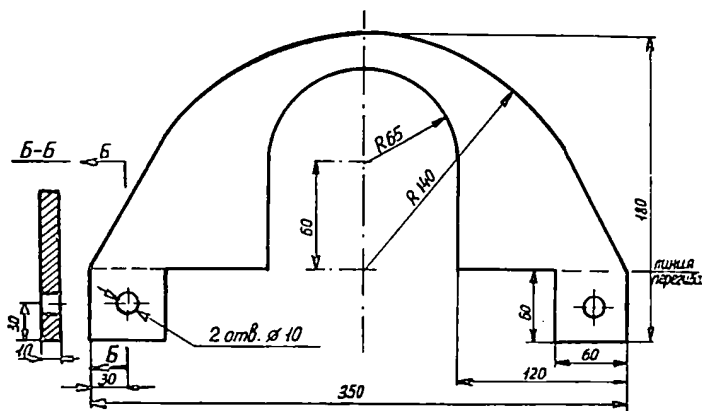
Уплотнительная прокладка корпуса подшипника барабана
